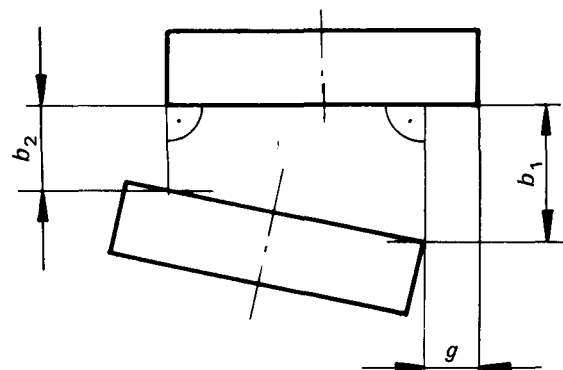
Défaut de contact dû à la déformation d'une machine à souder par bossages
